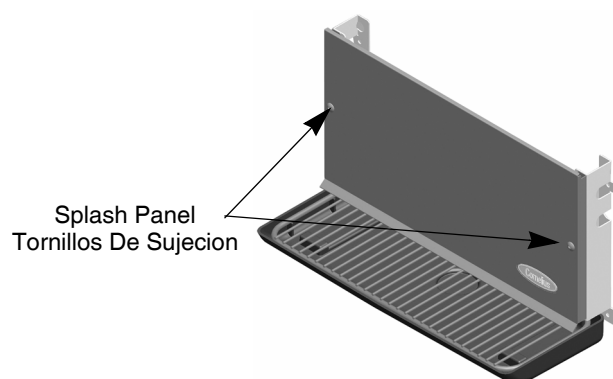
Tornillos De Montaje Para Panel De Toque Clásico
